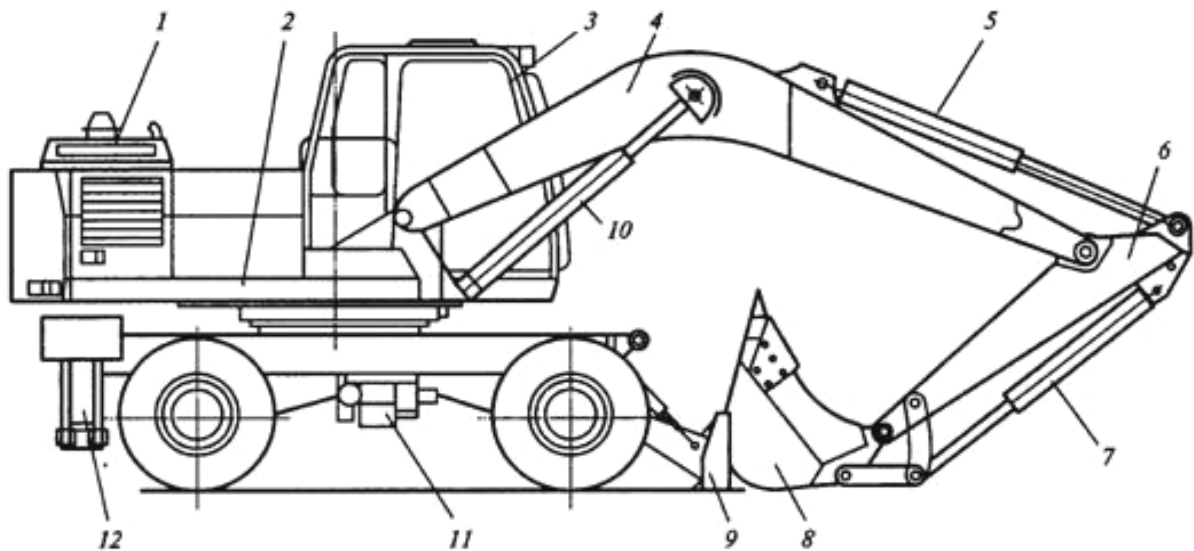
Одноковшовый полноповоротный пневмоколесный экскаватор ЕК-18: 1 – силовая установка; 2 – поворотная платформа; 3 – кабина оператора; 4 – моноблочная стрела; 5, 7, 10 – гидродомкраты рукояти, ковша и стрелы; 6 – рукоять; 8 – ковш; 9 – опора-отвал; 11 – пневмоколесное ходовое устройство; 12 – выносная опора
